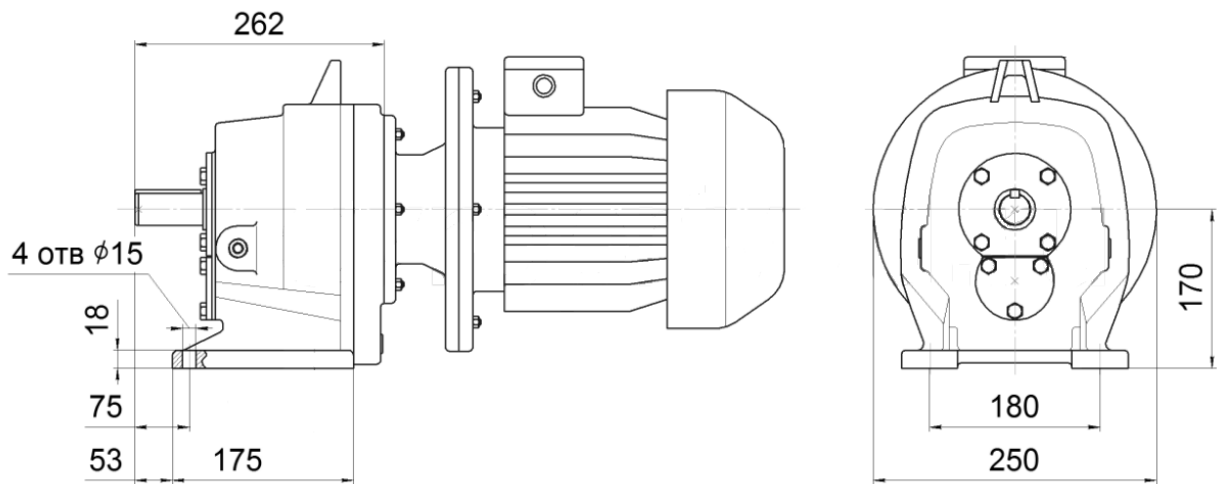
Основные габаритные и присоединительные размеры [6].
